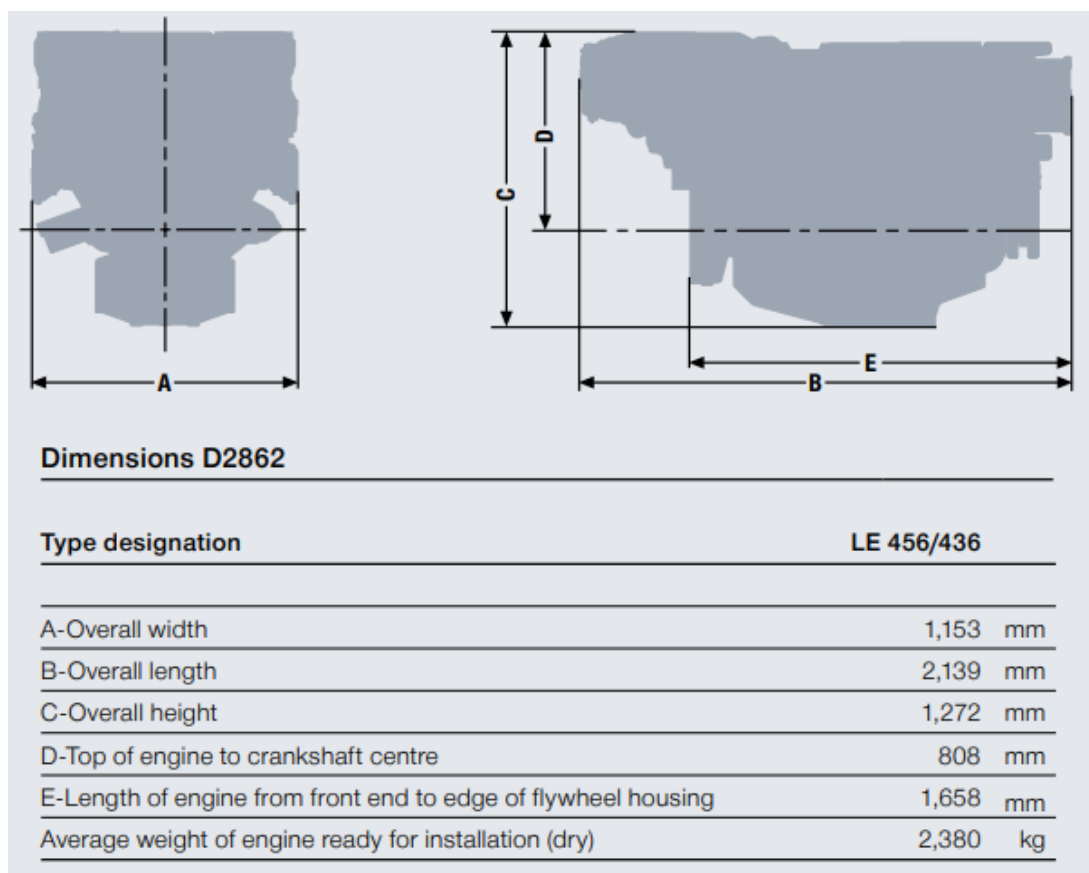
Dimensiones del motor MAN D2862 LE 436. Fuente: Pasch Naval.
